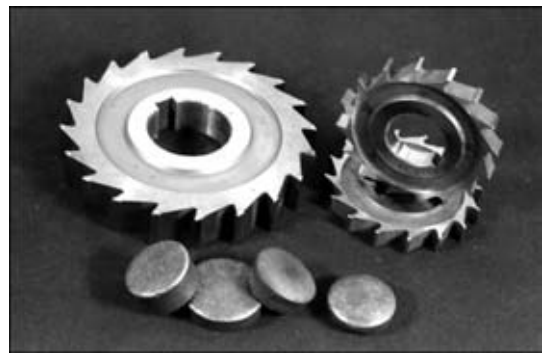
Режущий инструмент из быстрорежущей стали Р6М5 ЭППЕ
